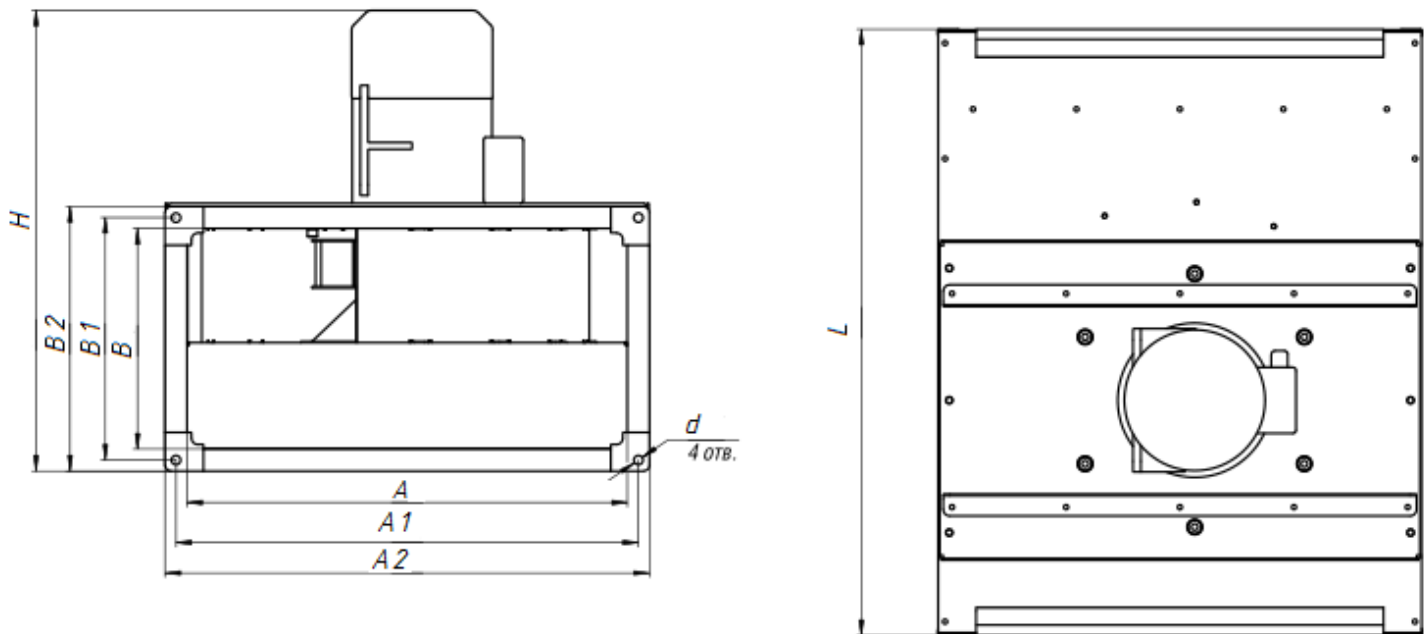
Габаритно-присоединительные размеры ВКПН-В
